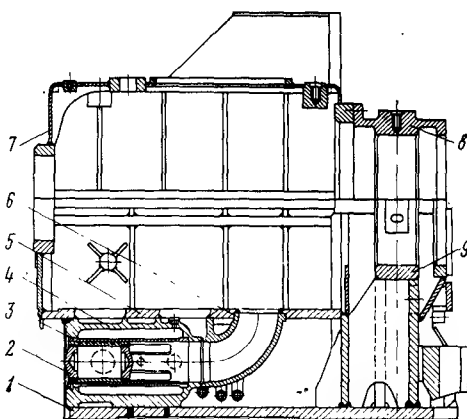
Сварной корпус переднего подшипника:
